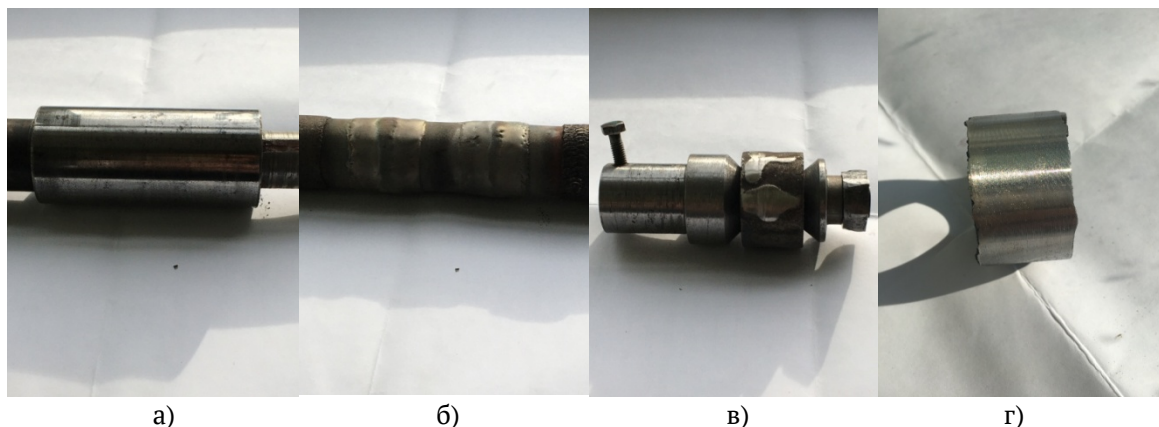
а) исходная деталь, б) плакированная деталь, в) деталь с цилиндрической базой для измерения, г) прошлифованная деталь до нужного размера
